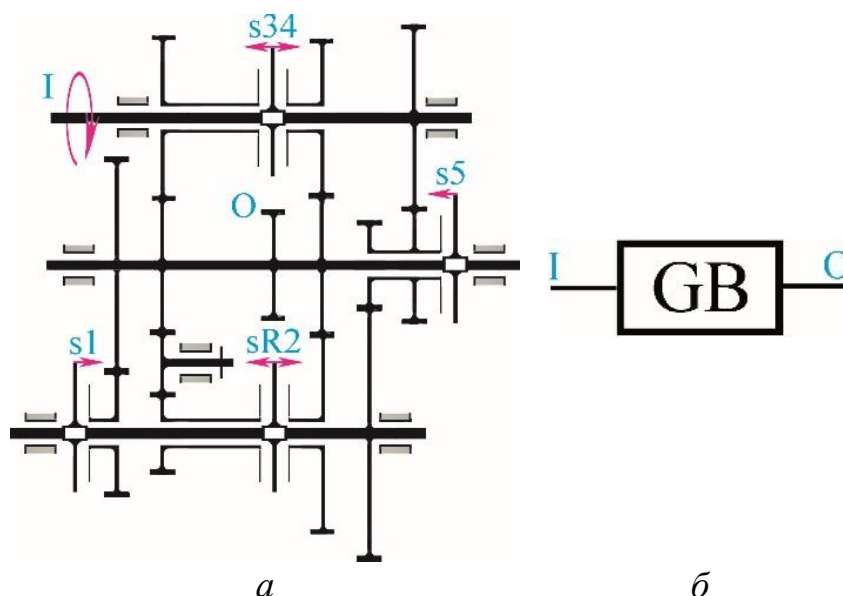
а – кинематическая схема 5-ти ступенчатой коробки передач с неподвижными осями колес; б – структурная схема вальной коробки передач.
